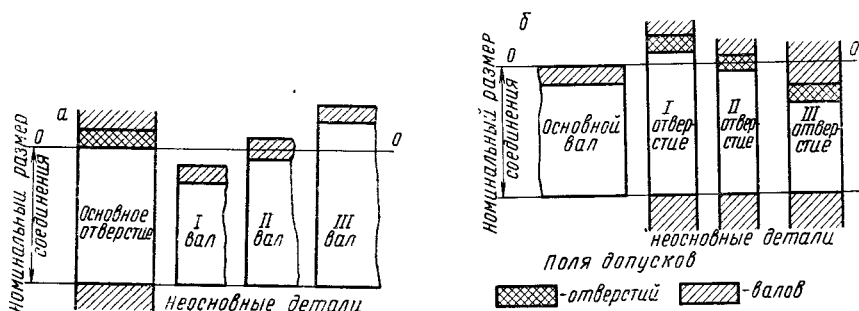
Схема расположения полей допусков отверстий и валов в различных системах:
